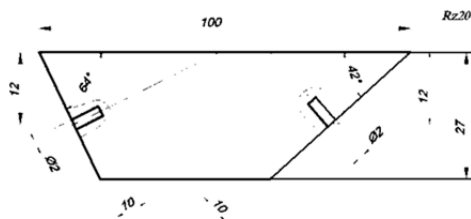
Эскиз настроечного стандартного образца предприятия с боковым цилиндрическим отверстием
